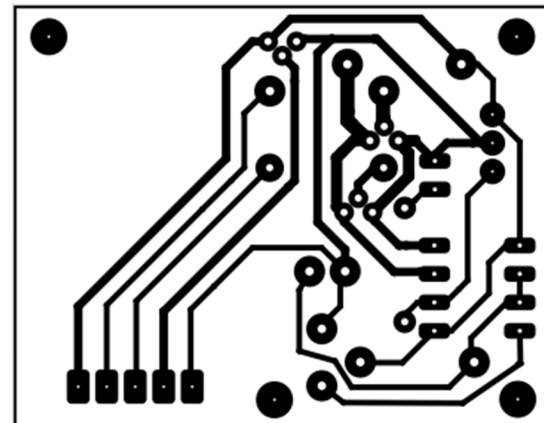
PCB2, Bottom view. Fuente: Autor.
